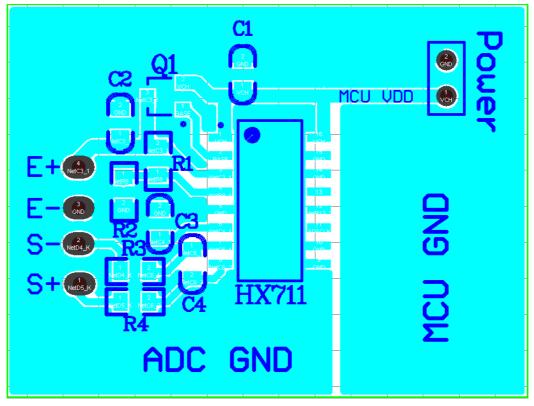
相关部分的 PCB 板参考设计线路图。图五为相应的单层 PCB 板参考设计板图。
